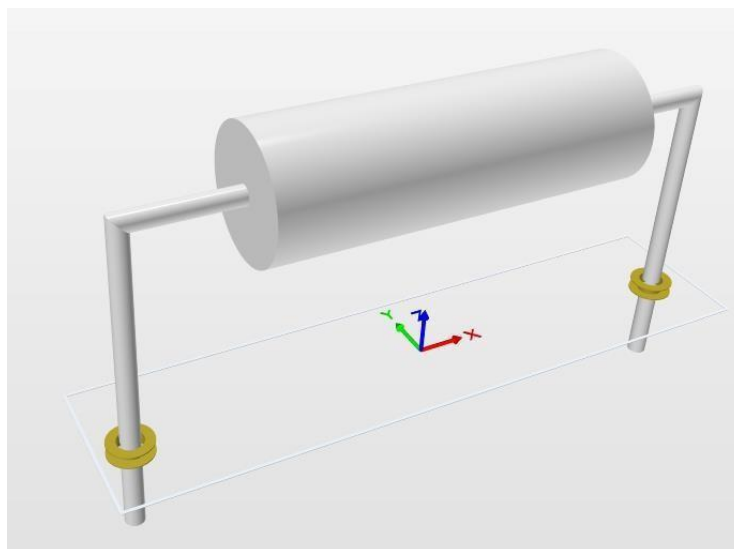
3D-модель запобіжника FU1 у середовищі Altium Designerr
